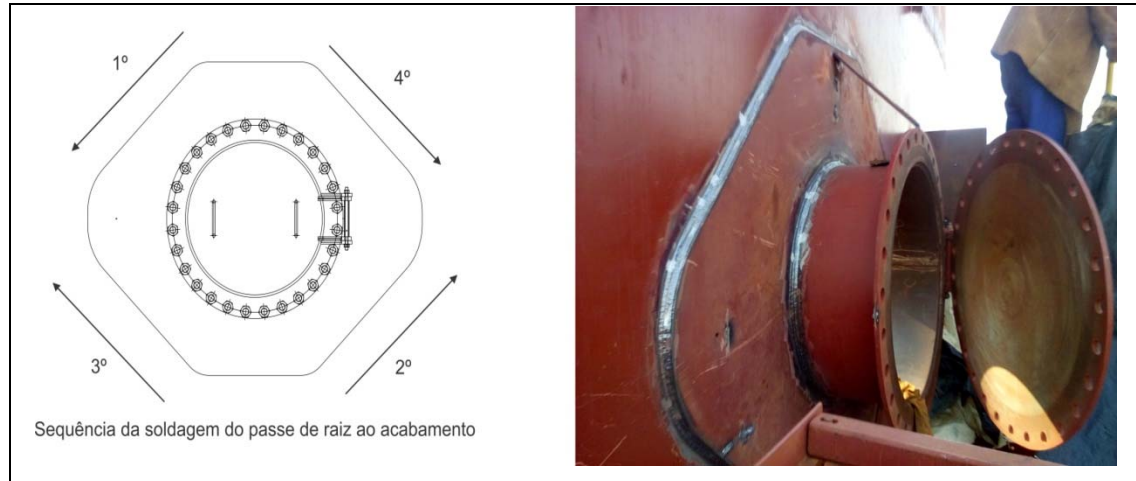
Travamento e sequência de soldagem da boca de visita. Autores
